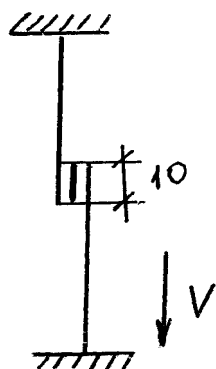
Схема испытания клеевого соединения на сдвиг
